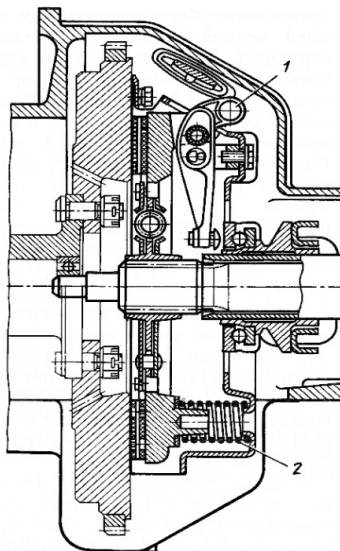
Полуцентробежное сцепление: 1 – центробежный грузик; 2 – нажимная пружина
